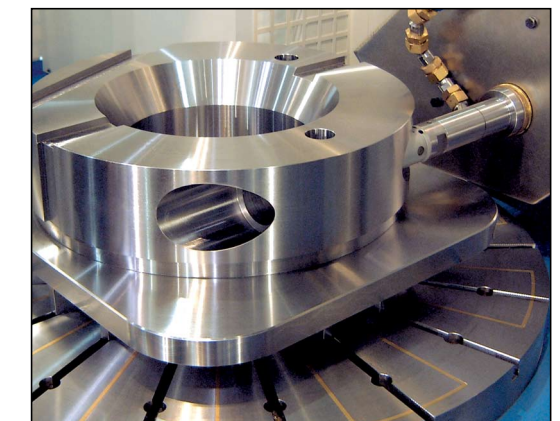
Ausspindeln einer außermittigen Bohrung im rechten Winkel zur Werkstückachse
